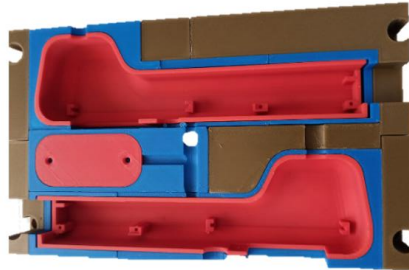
Prueba de dimensiones de la placa de cavidades con los componentes fabricados de la carcasa.
